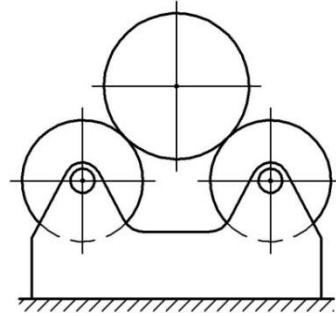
Альтернативна схема базування деталі за циліндричною поверхнею
